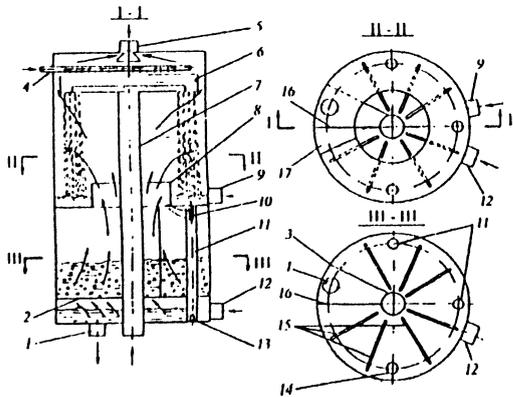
Общий вид двухступенчатого вакуумного деаэратора:
